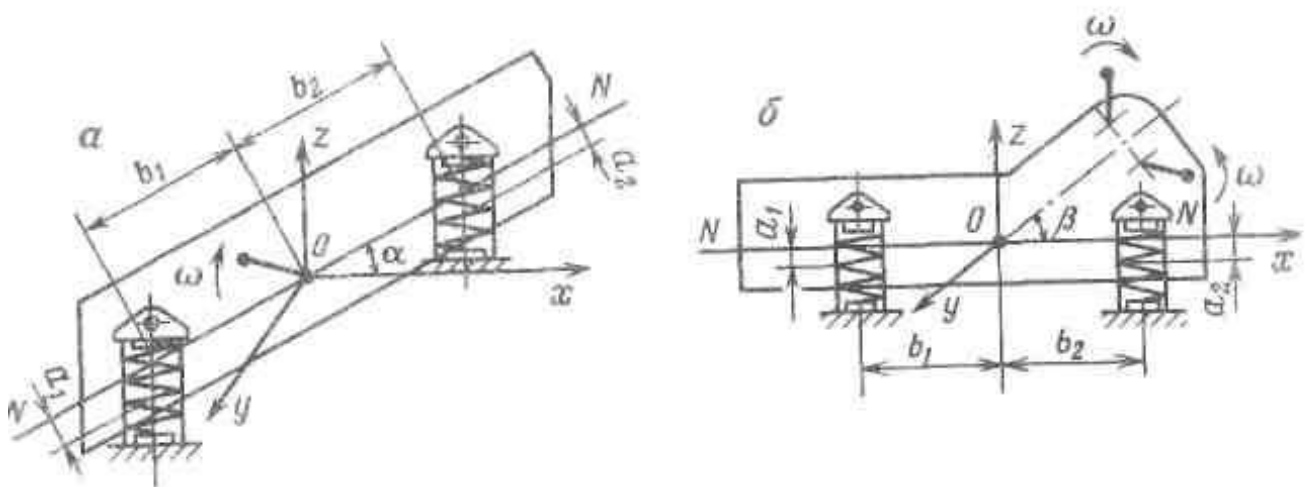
Схеми розташування віброізоляційних опор
